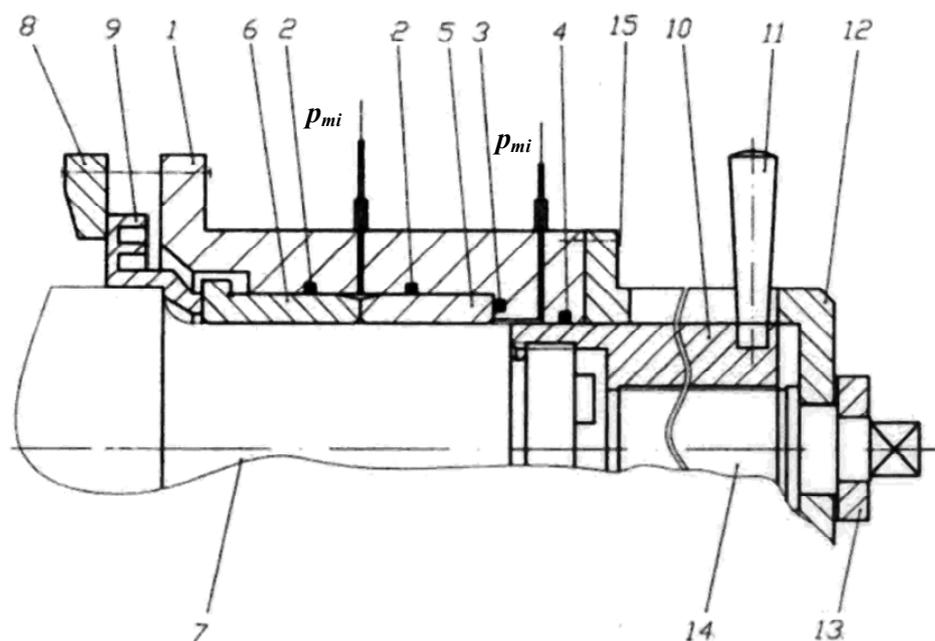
Принципиальная схема устройства для распрессовки колец буксовых подшипников и кольца лабиринтного уплотнения буксы колесной пары:
